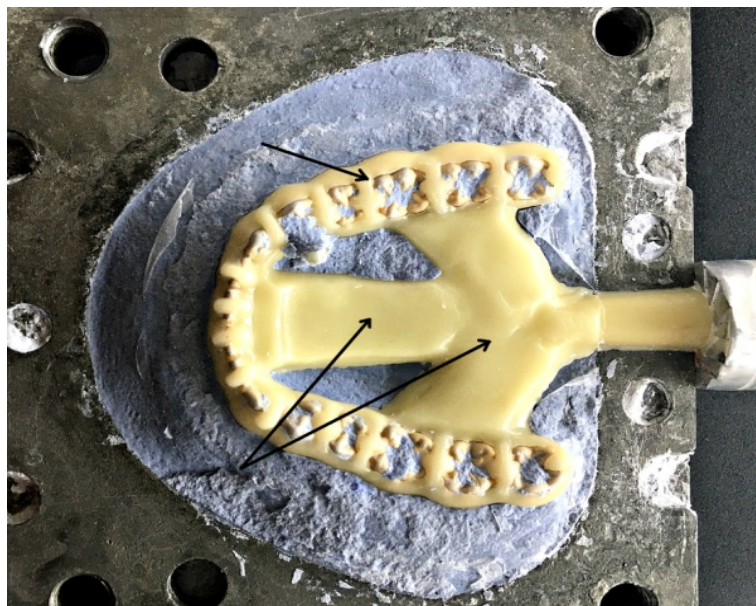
Отлитая конструкция шины с литникообразующей системой
